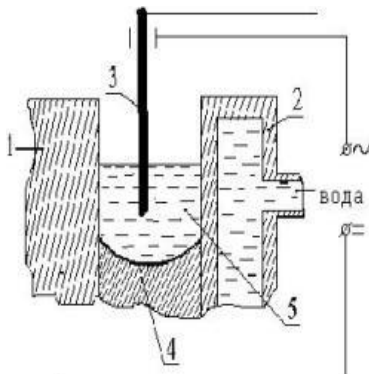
Схема электрошлаковой наплавки: 1.-деталь; 2.-медный кокиль, охлаждаемый водой; 3 электрод; 4.-наплавленный металл; 5.-расплав
